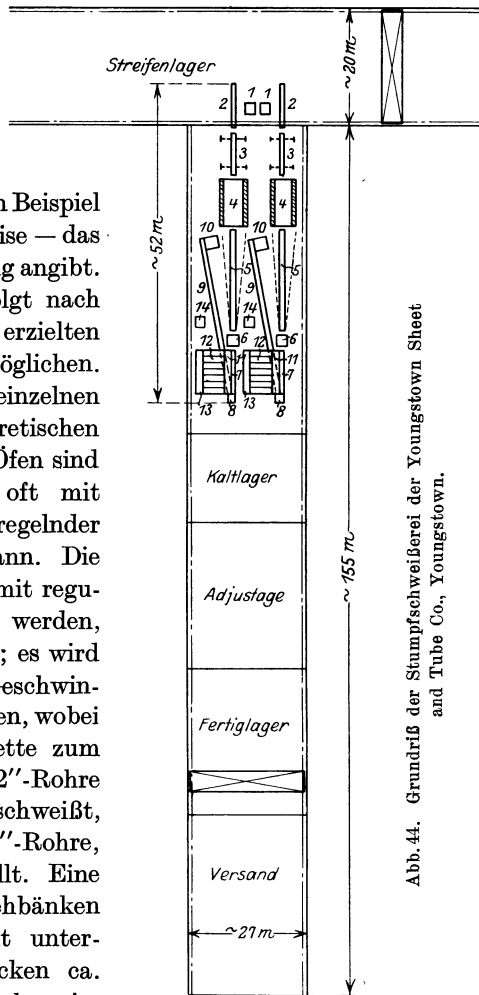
Grundriß der Stumpfschweißerei der Youngstown Sheet and Tube Co., Youngstown.
